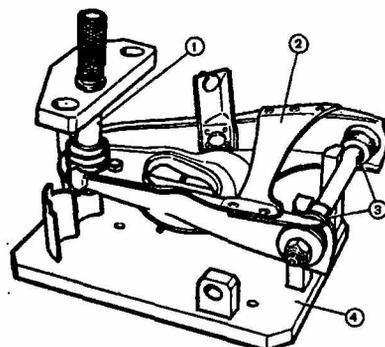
Проверка левого нижнего рычага: 1 - оправка для центровки шарового шарнира; 2 - нижний рычаг; 3 - отверстия для установочных пальцев приспособления А.95716; 4 - приспособление А.95716 для проверки рычагов
